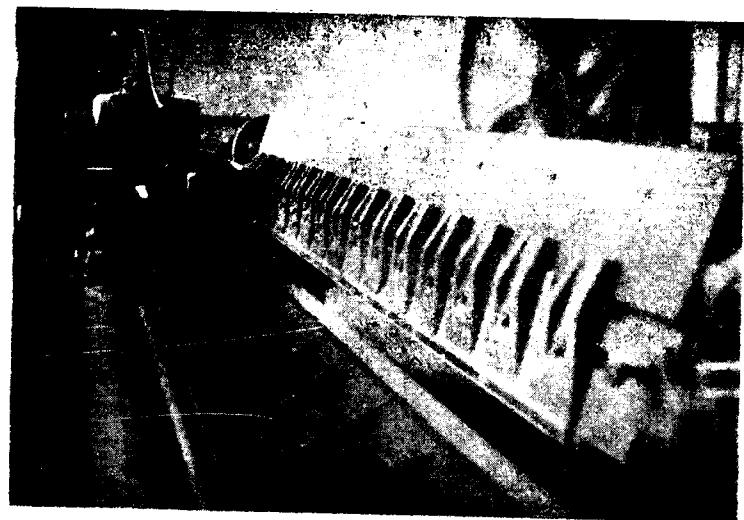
Furniermessermaschiene mit einem auf dem Tisch befestigten
